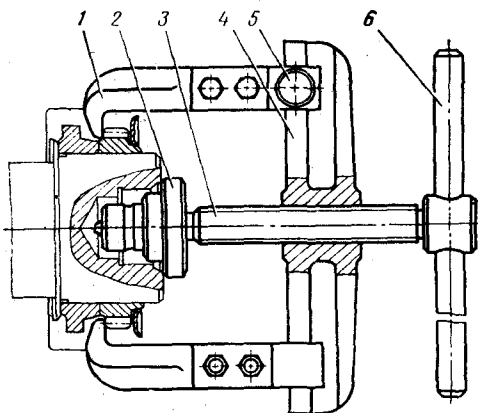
Снятие распределительной шестерни и заднего противовеса с коленчатого вала:
